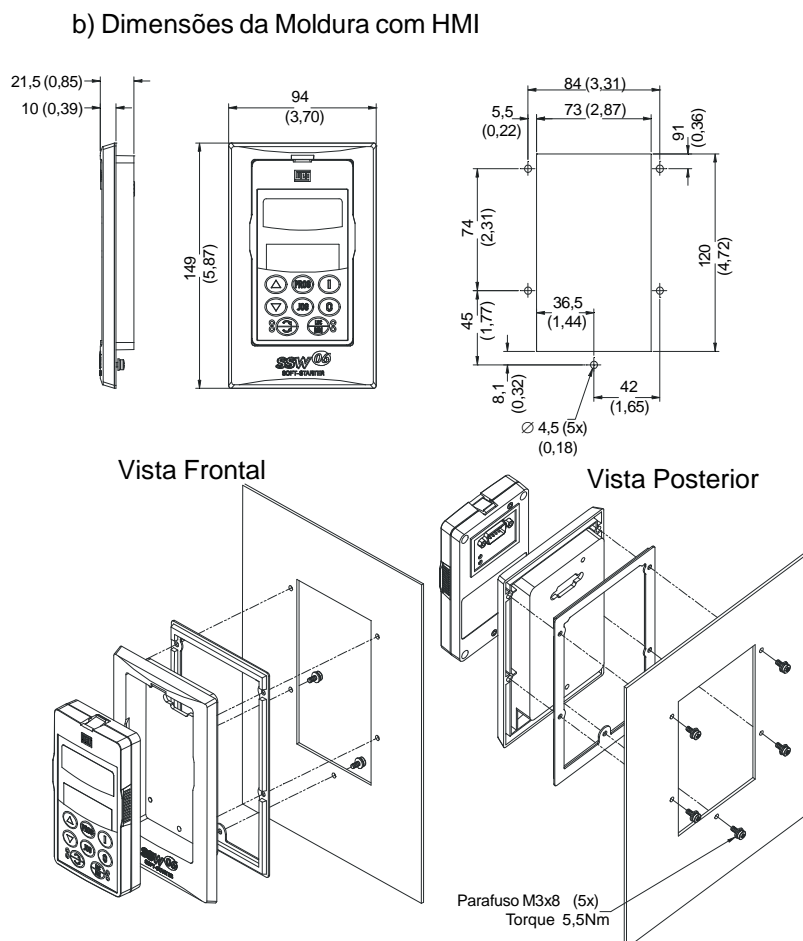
Dimensões da HMI em mm (in) e como instalar no painel com moldura
